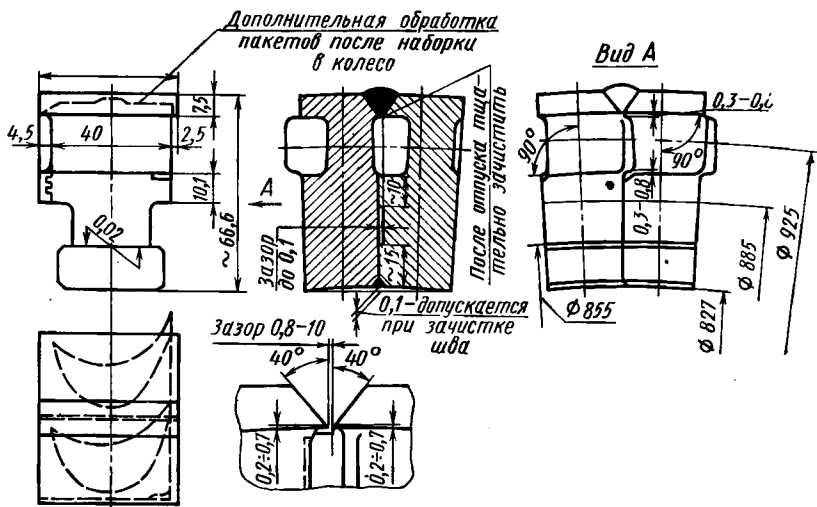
Сварной пакет лопаток 1-го венца колеса турбины 50 МВт
